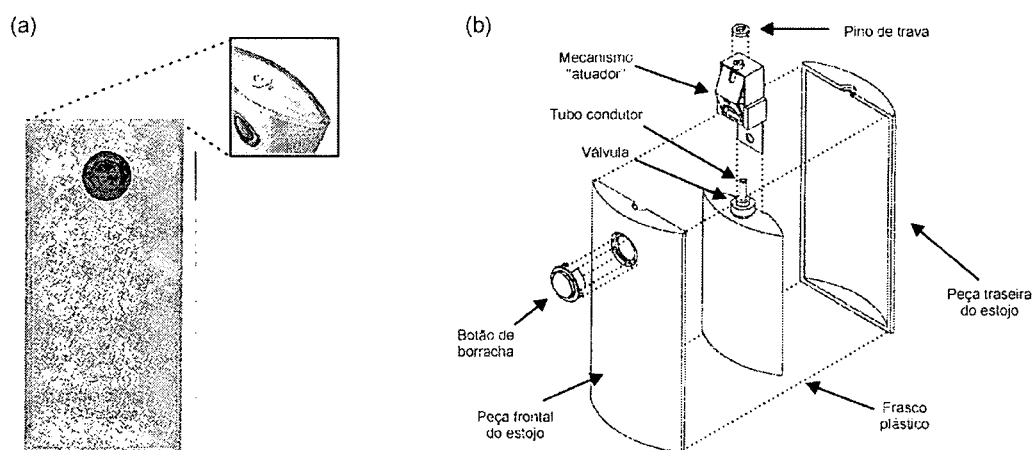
(a) Foto frontal da embalagem original do produto “Clipping” mostrando detalhe superior no quadro em destaque. (b) Perspectiva explodida da embalagem gerada em CAD. O “mecanismo atuador”, definido como o “Módulo Base” (MB), está também representado no desenho.
